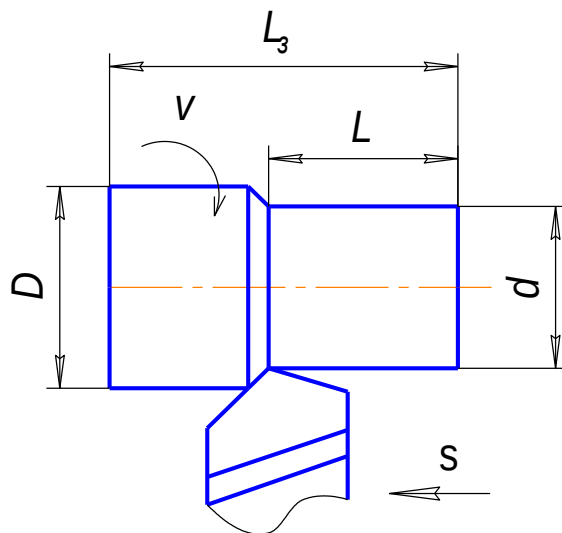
Схема обработки заготовки к задаче 1
